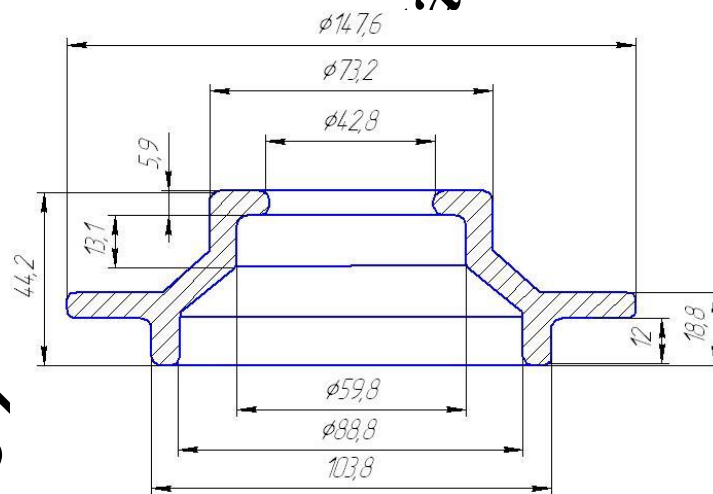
Ескіз заготовки при литті в кокіль
